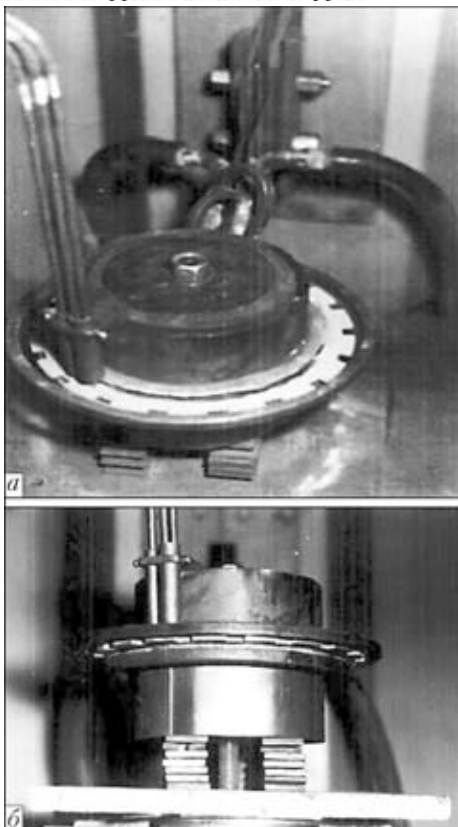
Устройство для наплавки диска в двухвитковом кольцевом индукторе [34]: а — вид сверху; б — сбоку
